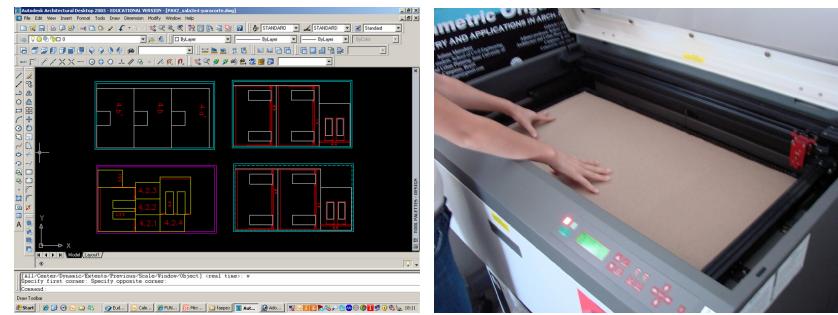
Desenho das peças a serem cortadas; cortadora a laser ULS X-660.
